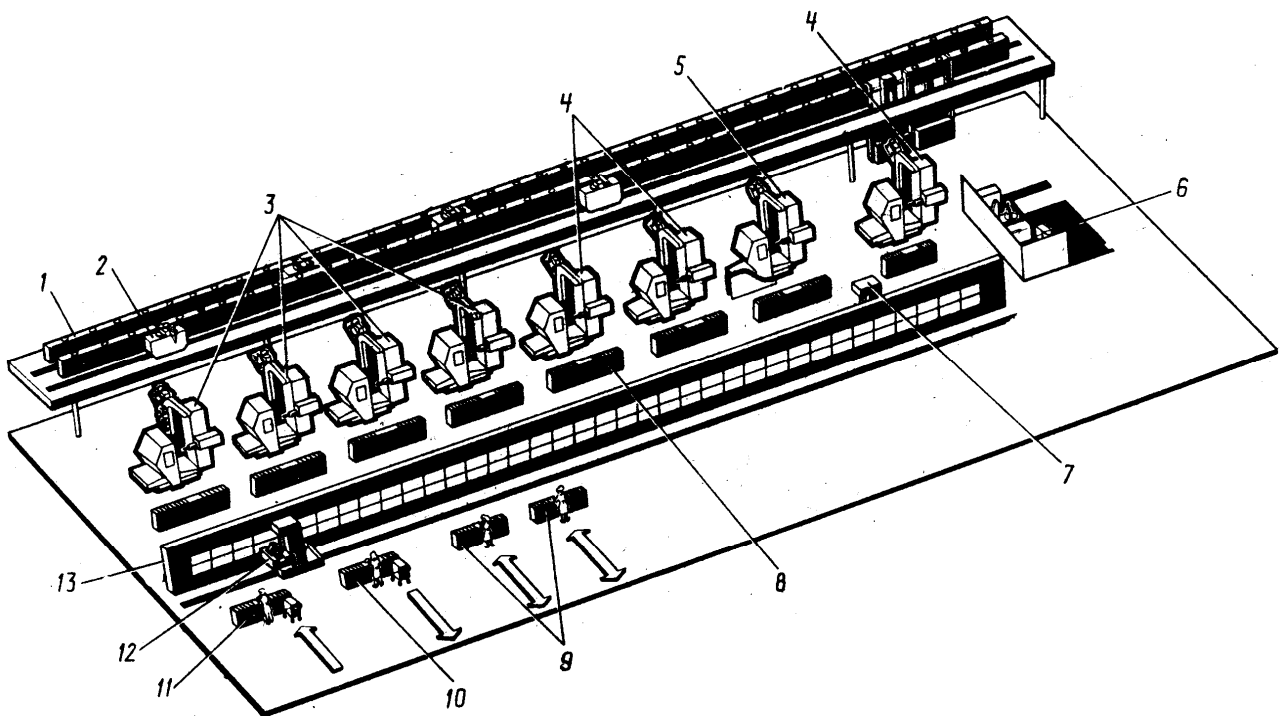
Схема автоматизованого комплексу АЛП-3-2 для оброблення широкої номенклатури корпусних деталей
